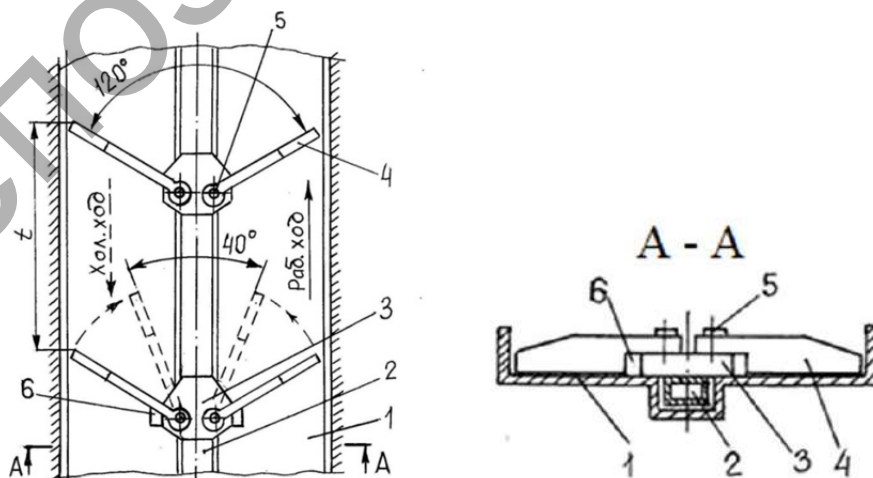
Фрагмент скребкового штангового транспортёра (вид сверху)
